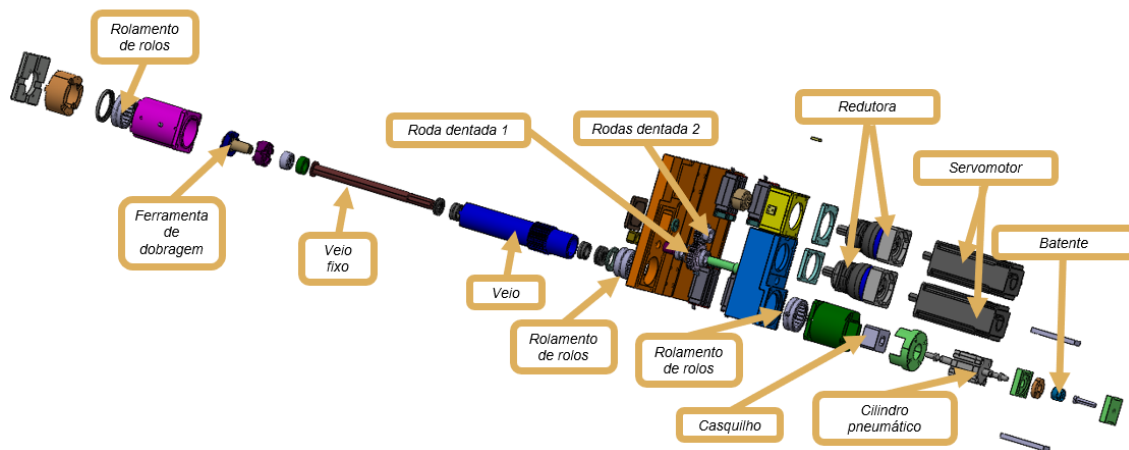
Vista explodida do dispositivo de dobragem CNC
